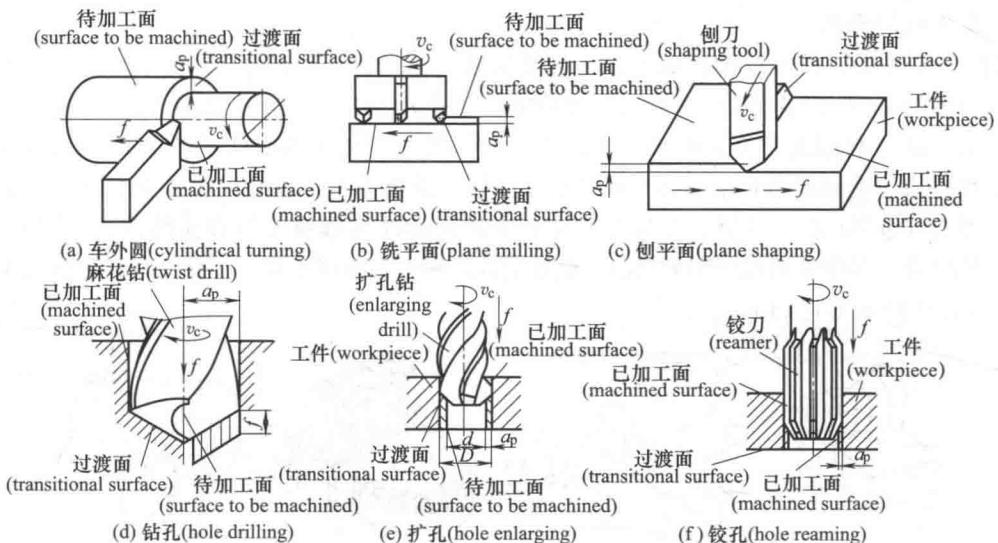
加工工件表面的定义 (definition of surfaces on workpiece in machining)
